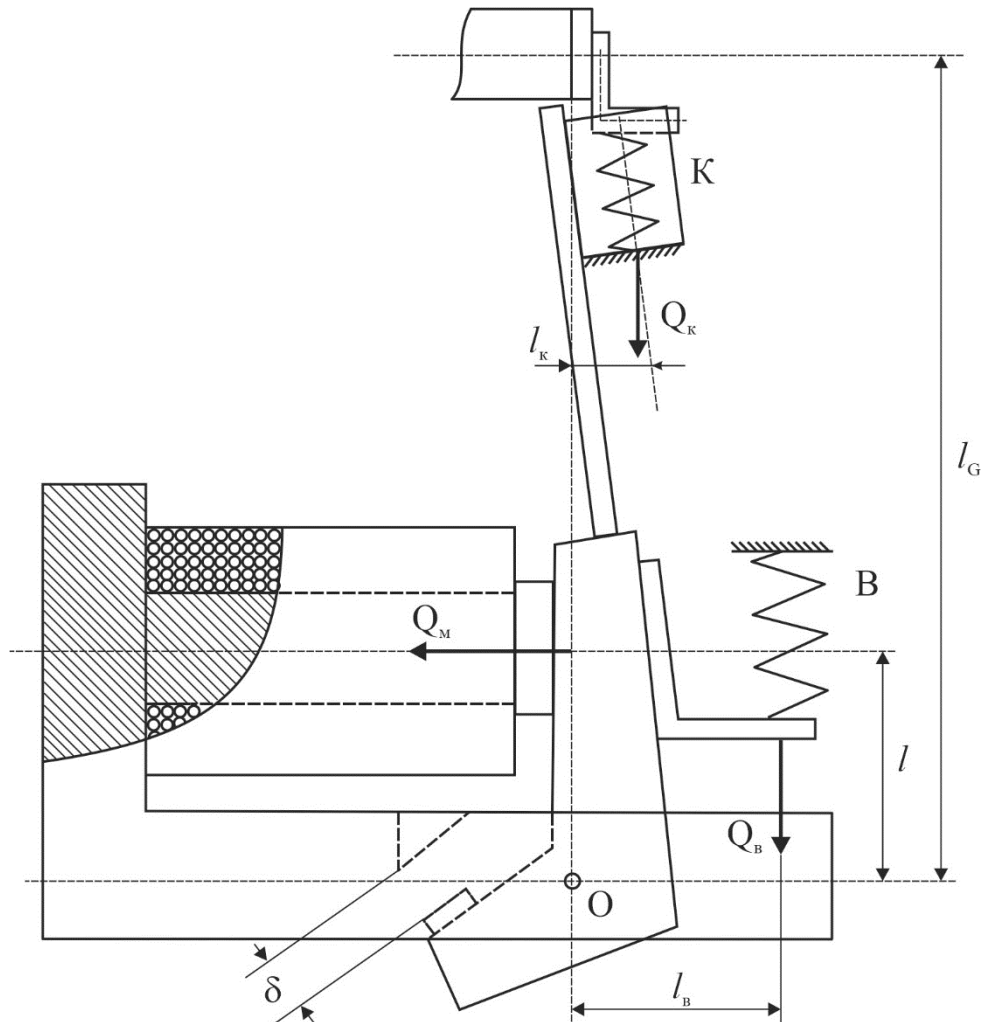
Кінематична схема електромагнітного привода контактора
